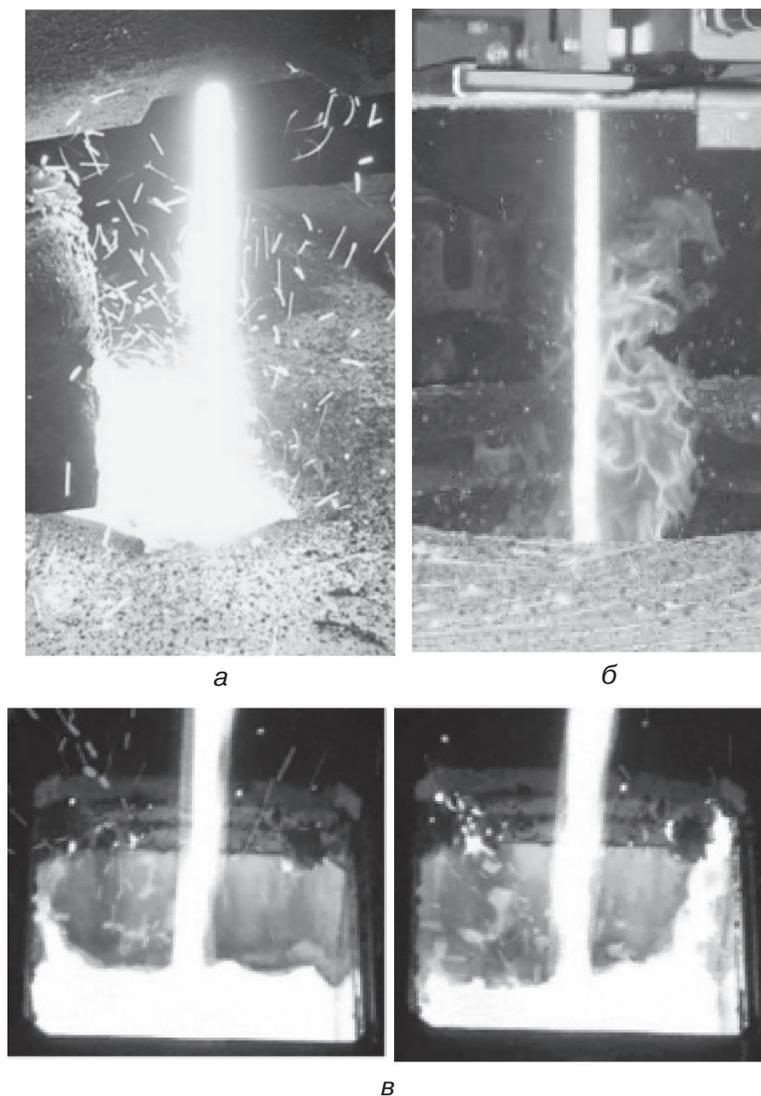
Разливка на сортовых МНЛЗ открытой струей: а – компактная струя; б – «веерная» струя; в – наплески, брызго- и волнообразование на зеркале металла в кристаллизаторе
